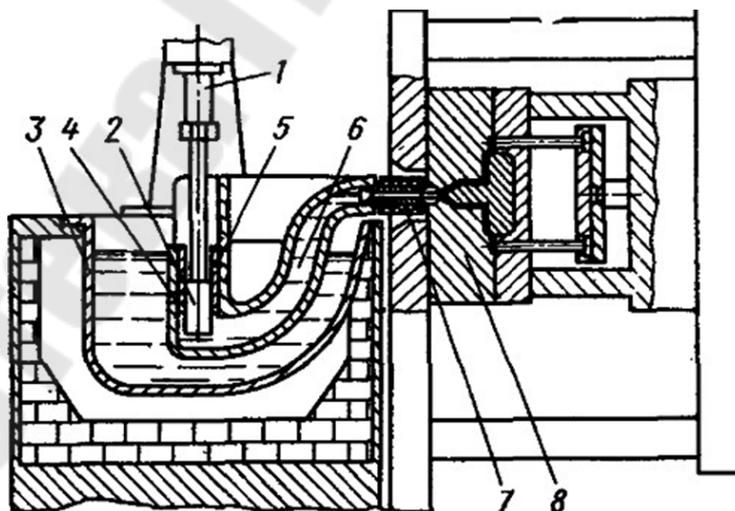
3 Схема машины для литья под давлением с горячей камерой прессования: 1- прессовый цилиндр; 2- прессовый плунжер; 3-чугунный тигель; 4- отверстие для поступления металла в прессовый стакан; 5- прессовый стакан; 6- гузек (металлопровод); 7- мундштук; 8- пресс-форма.
